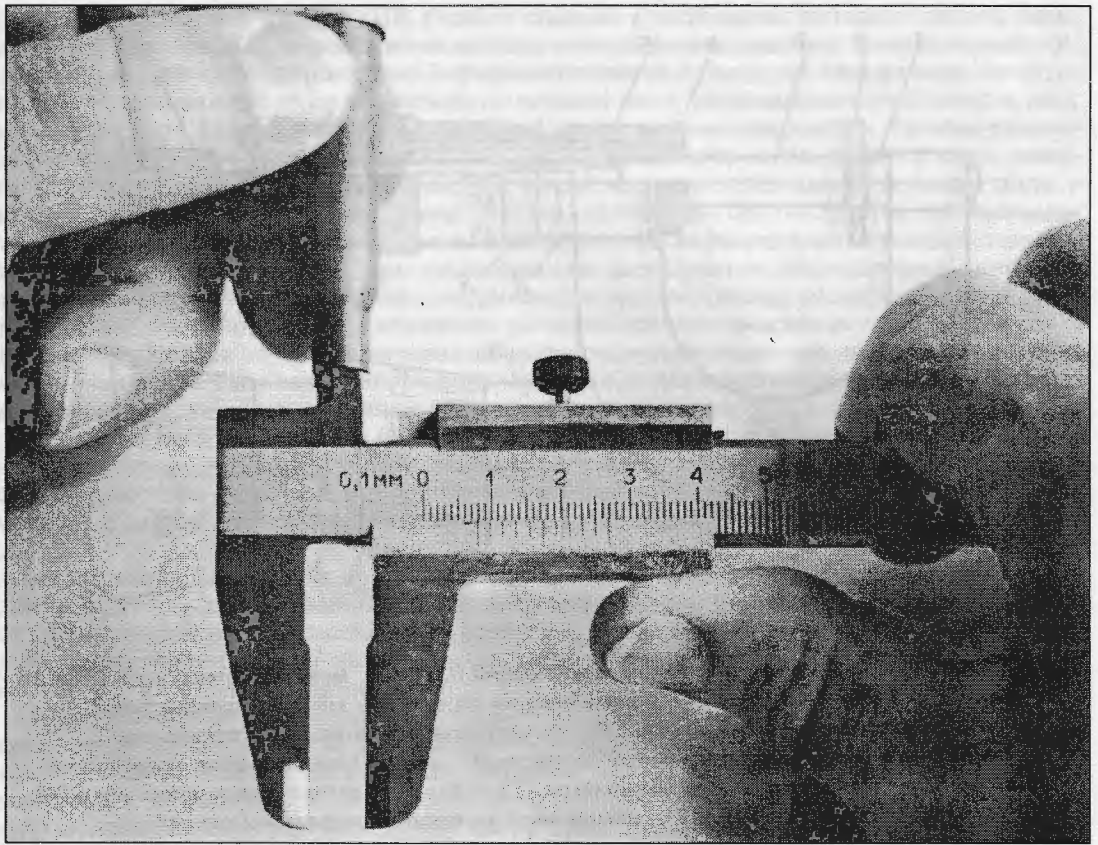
Штангенциркуль: 1 – масштабна лінійка-штанга, 2 – видвижна лінійка, 3 – рамка з ноніусом, 4 – рухома губка, 5 – внутрішні вимірювальні поверхні, 6 – нерухома губка штанги, 7 – зовнішні вимірювальні поверхні губок.
